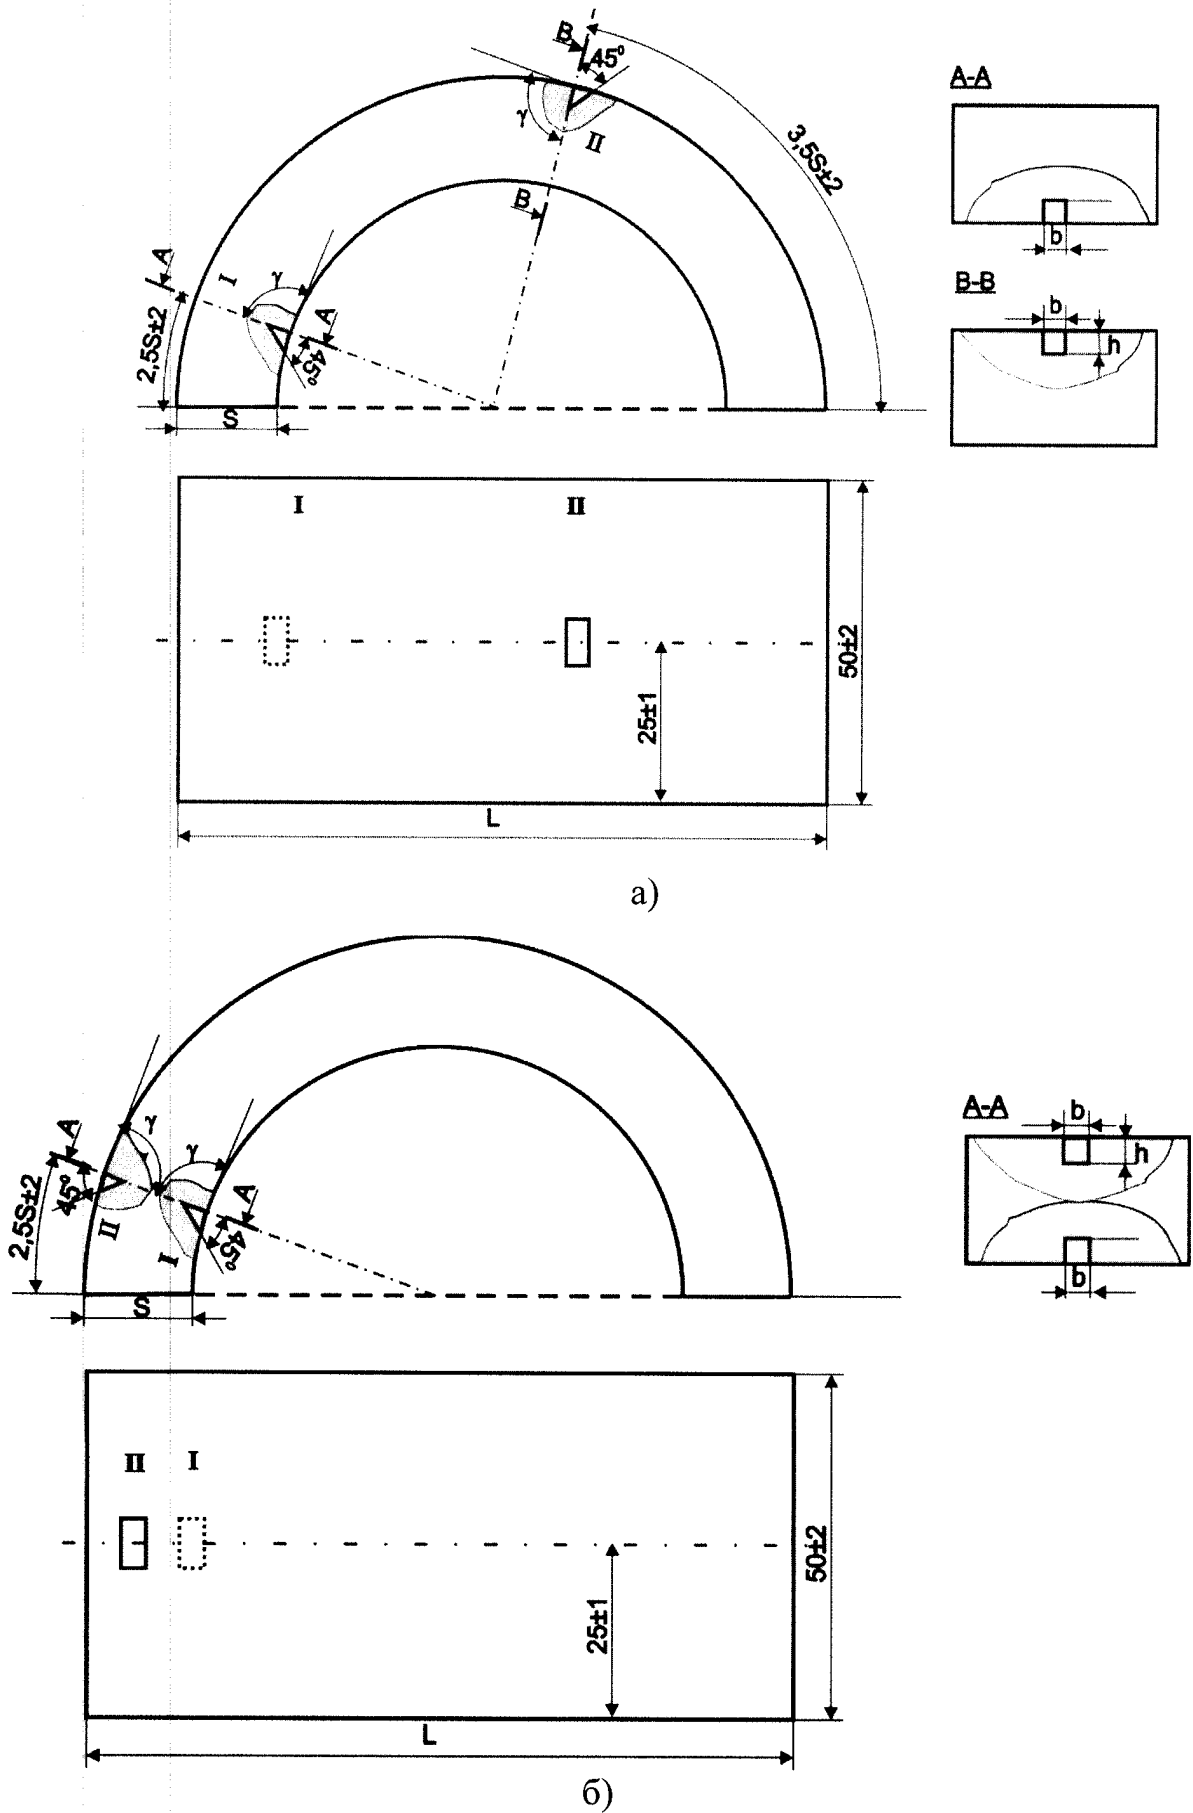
Стандартный образец предприятия с зарубками для УЗК гибов труб
